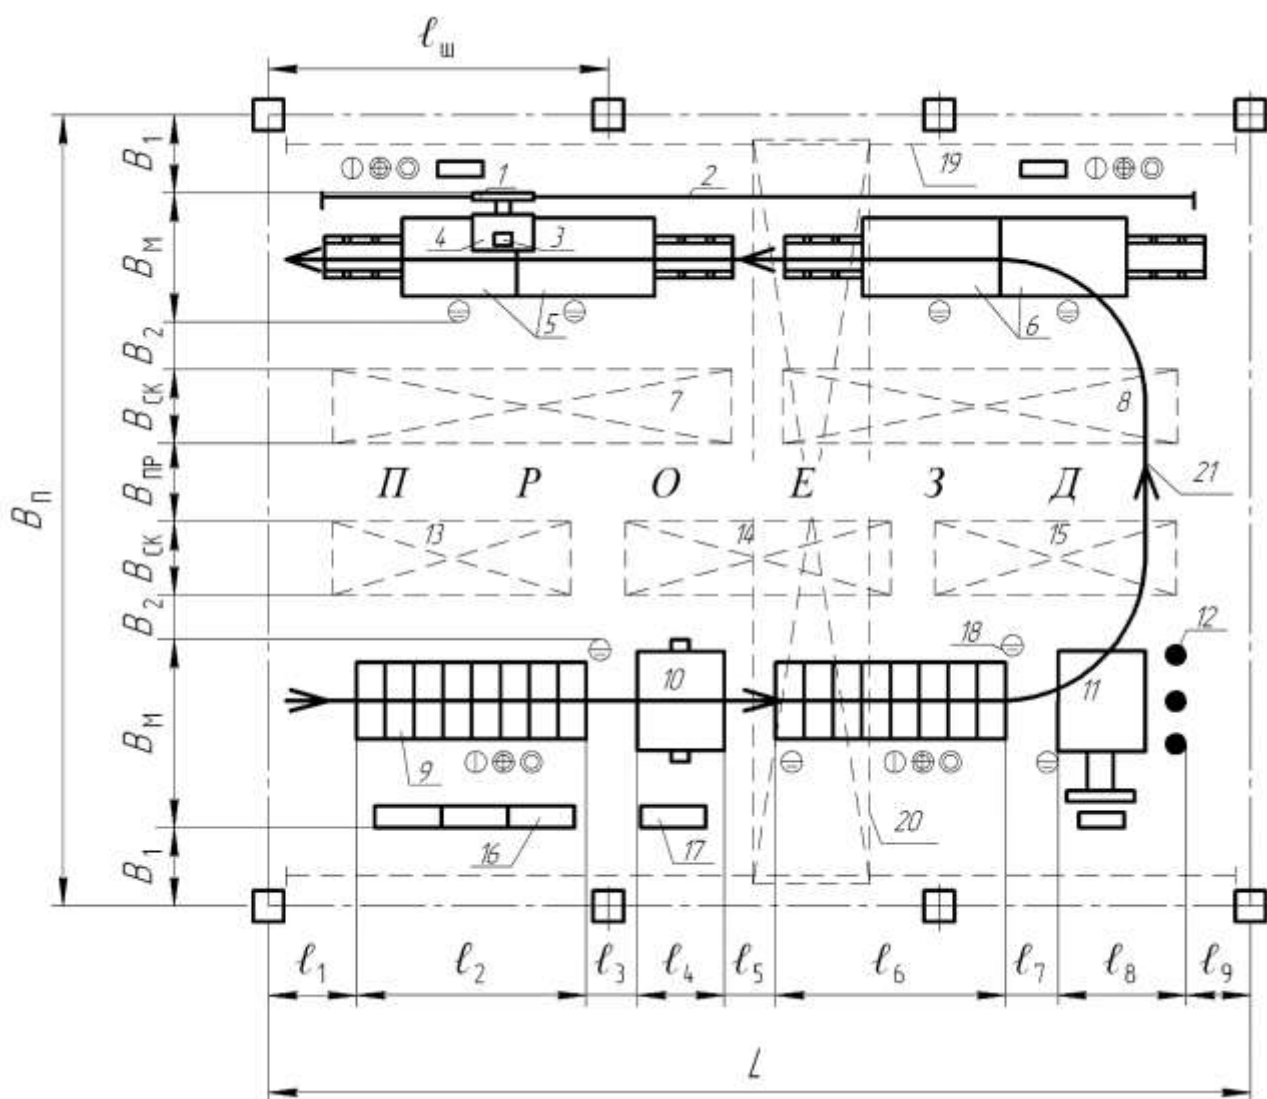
Планировка участка заготовки, сборки и сварки обечаек: 1 – велосипедная тележка с балконом; 2 – направляющий рельс; 3 – сварочный трактор (головка); 4 – роликовый стенд; 5 – свариваемые обечайки; 6 – обечайки для сборки под сварку; 7 – складочное место для сваренных обечаек; 8 – складочное место для вальцованных обечаек; 9 – рольганг; 10 – гильотинные ножницы; 11 – листогибочная машина с откидным верхним валком; 12 – поддерживающее устройство; 13 – складочное место для поступающих листов; 14 – складочное место для обрезанных в размер листов; 15 – складочное место для вальцованных обечаек; 16 – стеллажи для инструментов и оснастки; 17 – шкаф управления; 18 – рабочее место; 19 – подкрановый путь; 20 – мостовой кран; 21 – направление грузопотока.
